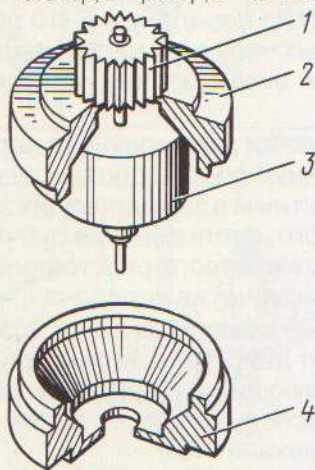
Ротор шагового двигателя с вынесенной катушкой:
